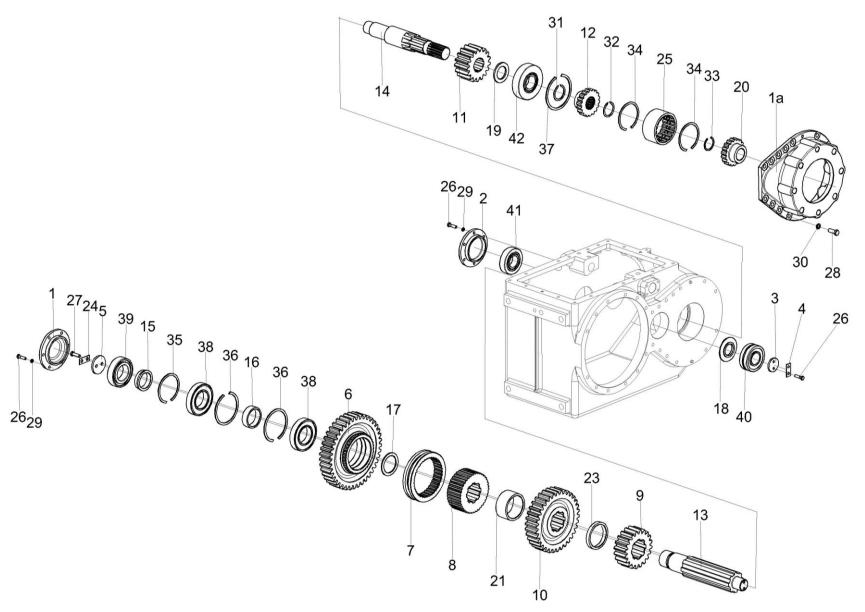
Коробка передач КВК 0106030 (лист 2)
